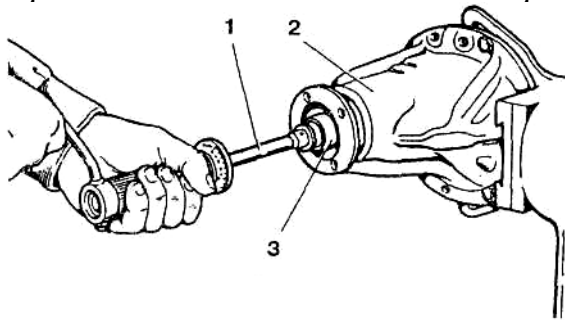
Проверка предварительного натяга подшипников ведущей шестерни: 1—динамометр 02.7812.9501; 2 — картер; 3 — переходная втулка
